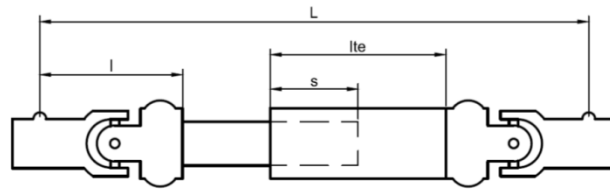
Nomenclatura de las dimensiones del eje cardán.
